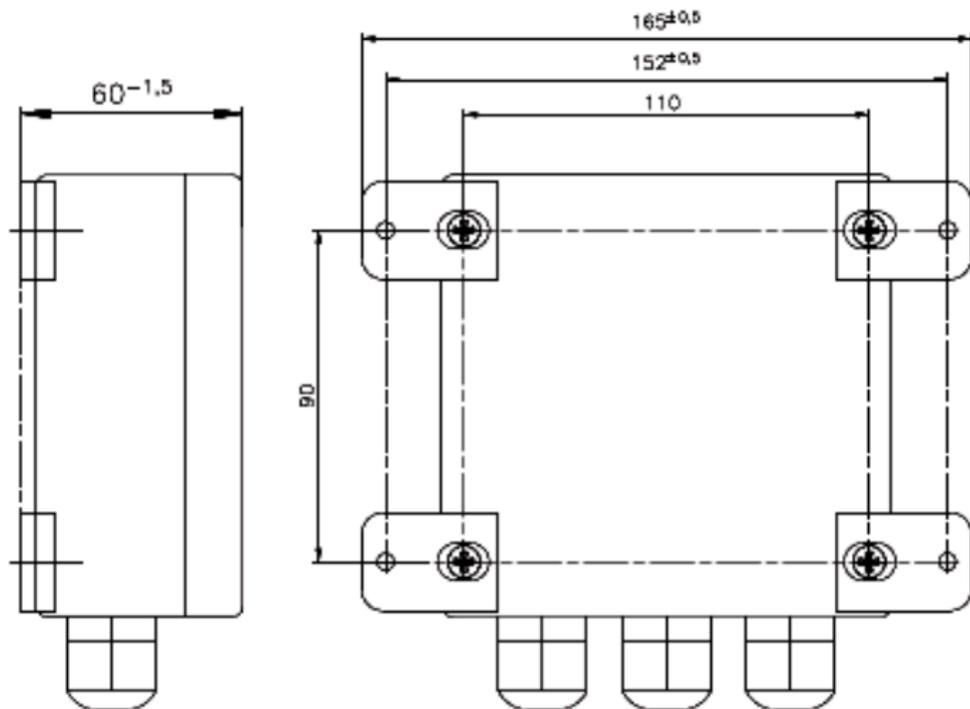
Габаритные размеры для крепления корпуса типа К1
